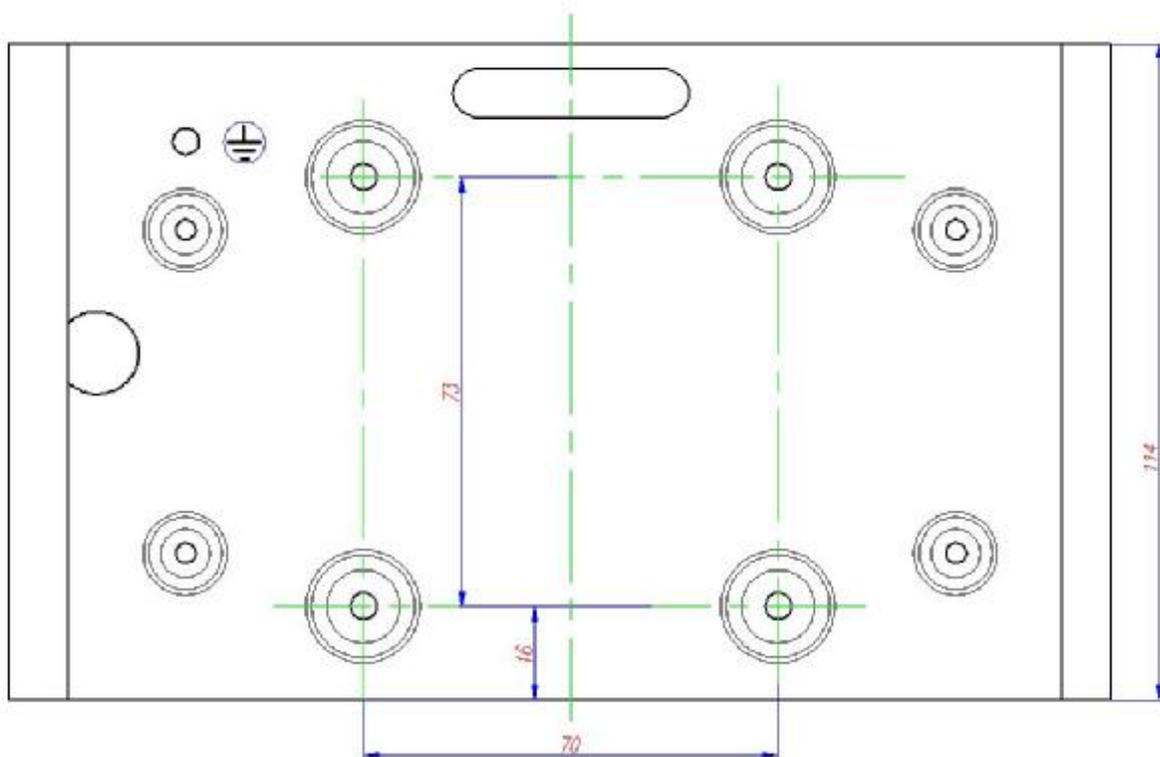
Основание корпуса РНП-01 с размещением крепежных отверстий
